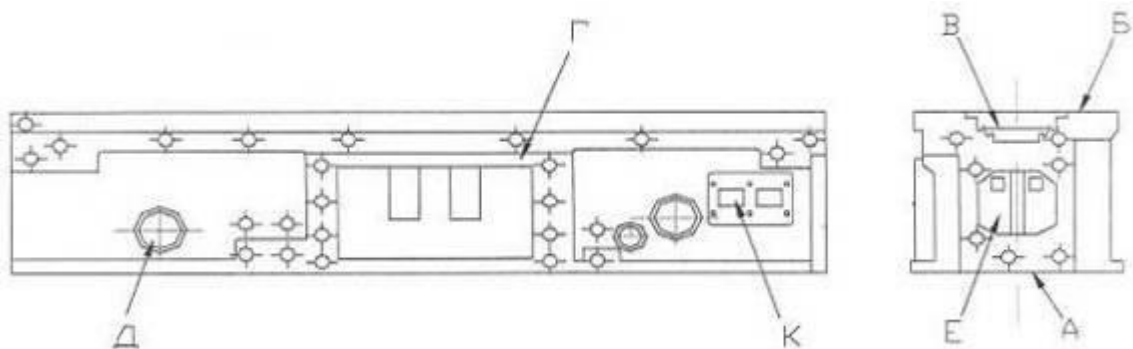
Станина для без консольних вертикально - фрезерних верстатів.
